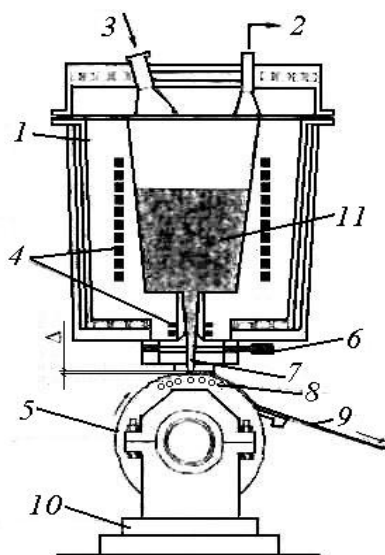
Схема установки для получения аморфной металлической ленты конструкции ВНИИЛИТМАШ
